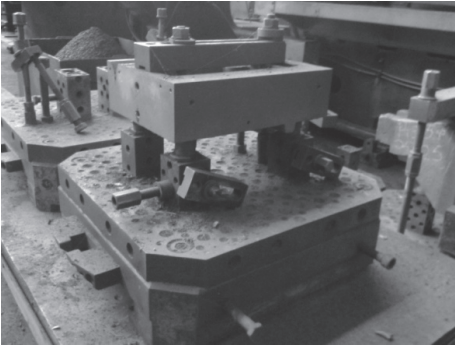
Универсально-сборные приспособления УСПО-16
